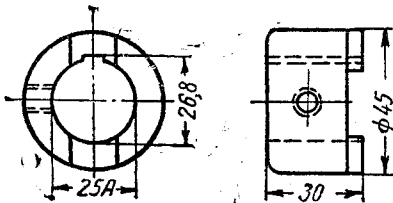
Оправка для фрезерования кулачков муфты переключения:
